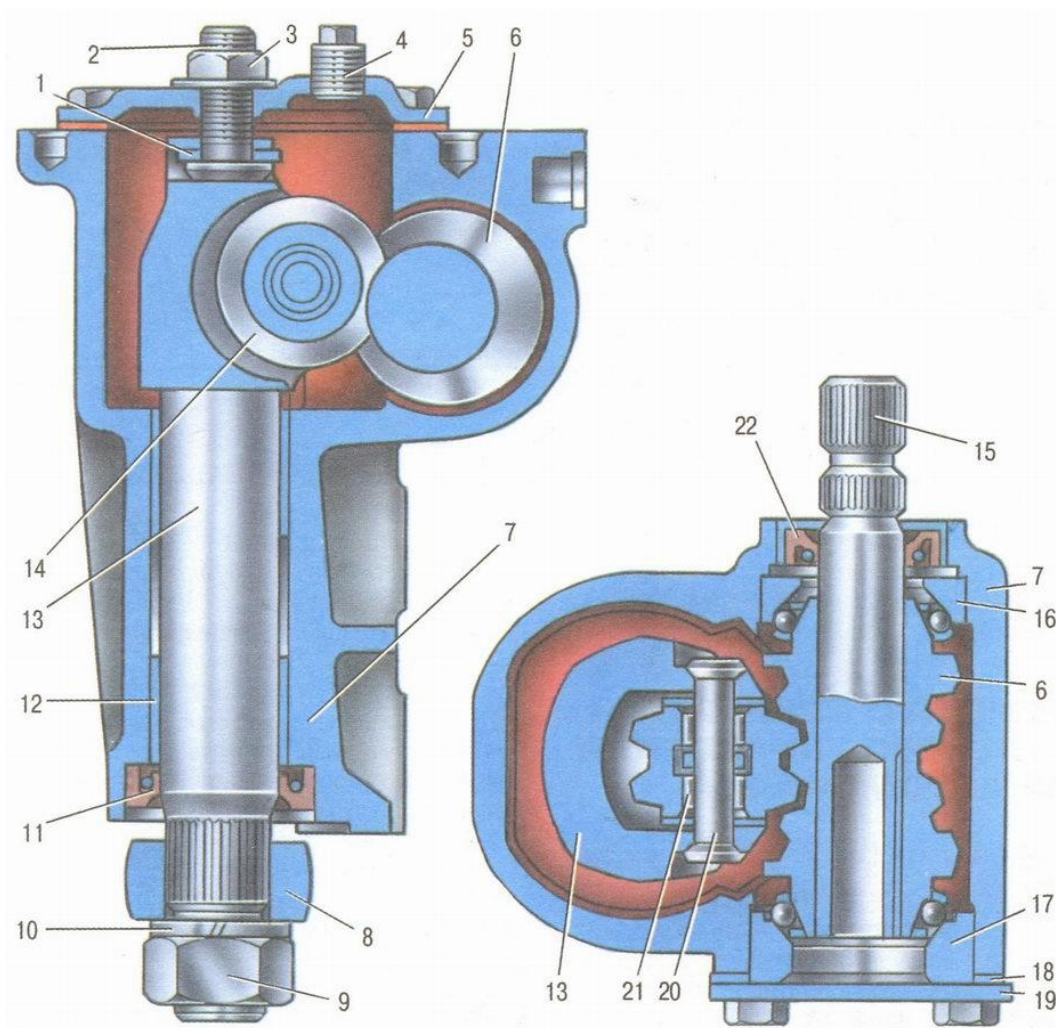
Деталі рульового механізму ВАЗ 2106:
